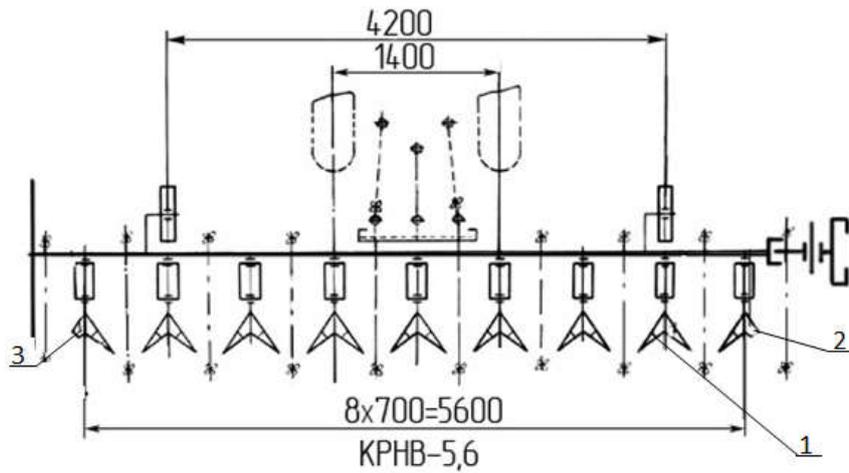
Схема розташування корпусів підгортальних для міжрядь 70 см:
